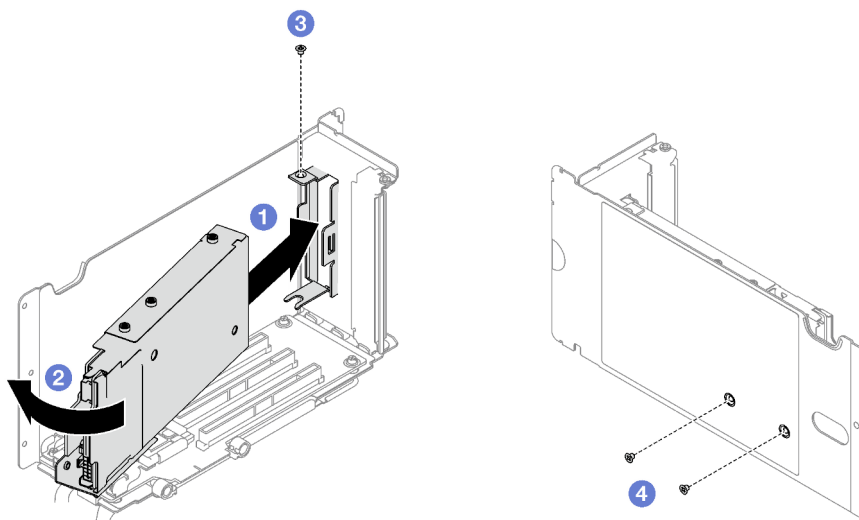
Installation du boîtier d'unités de disque dur 7 mm
